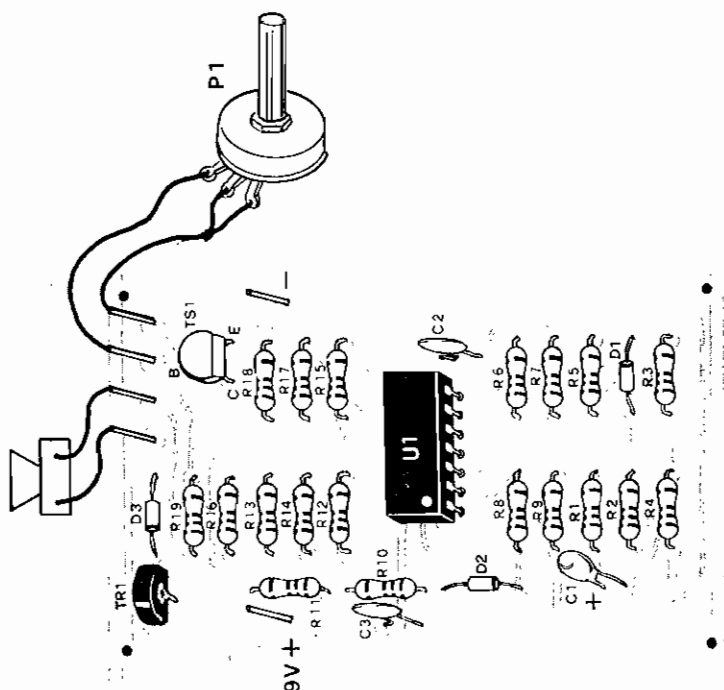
vista dell'assemblaggio della basetta MK 185.
